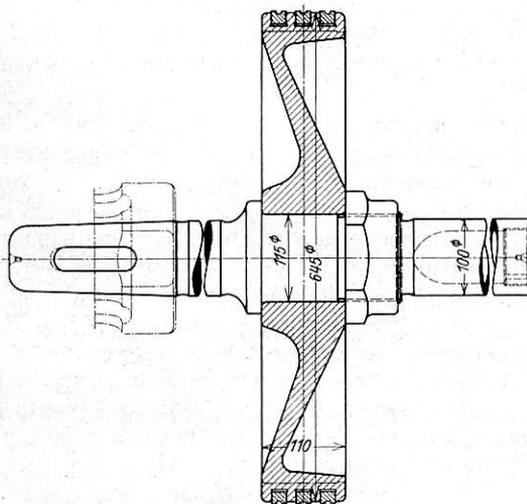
Kolben mit Kolbenstange der Reihe 01.
